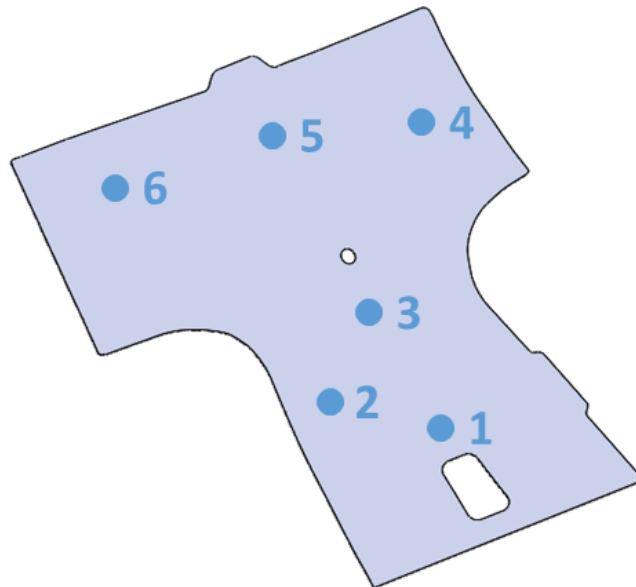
Schweißpunkte der Thermoelemente
